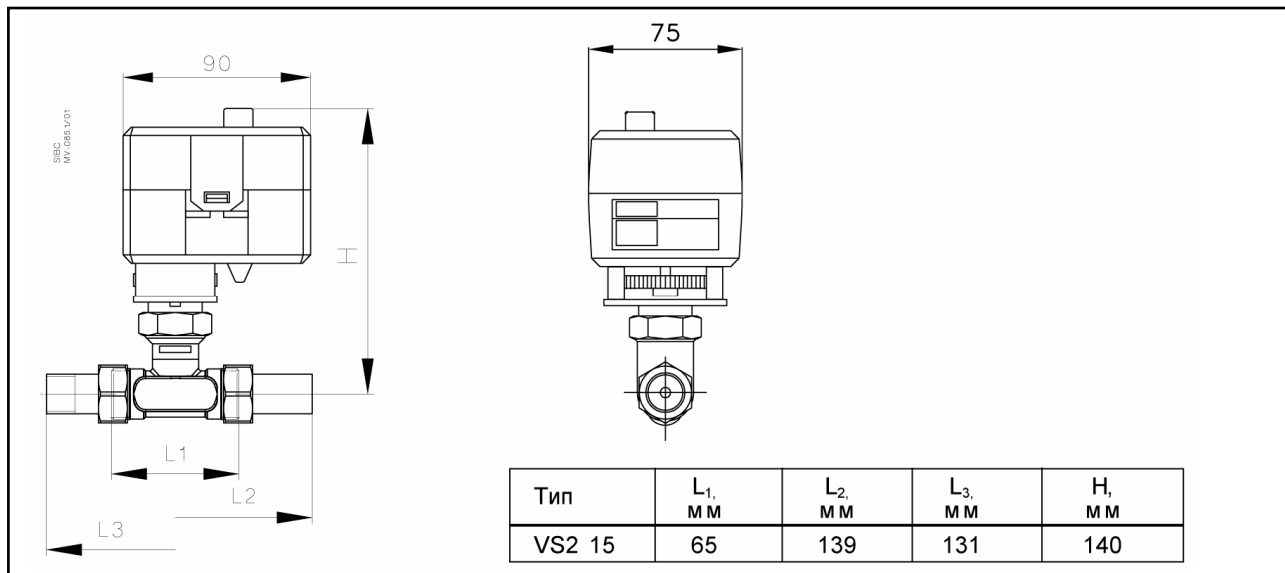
Габаритные и присоединительные размеры AMV 100 с клапаном VS2.
